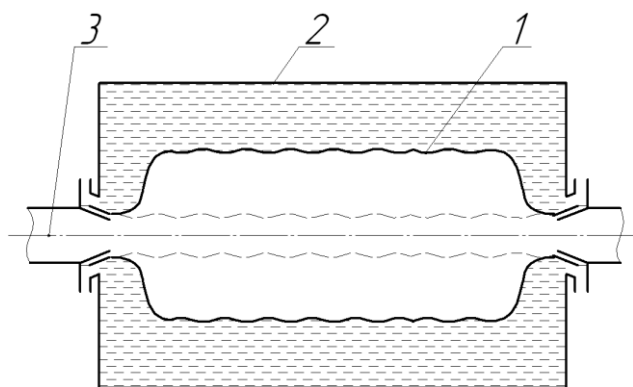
Гідравлічний компенсатор з трубчастою діафрагмою, яка здатна збільшувати свій діаметральний розмір: 1 – трубчаста діафрагма; 2 – корпус компенсатора; 3 – напірний трубопровід
